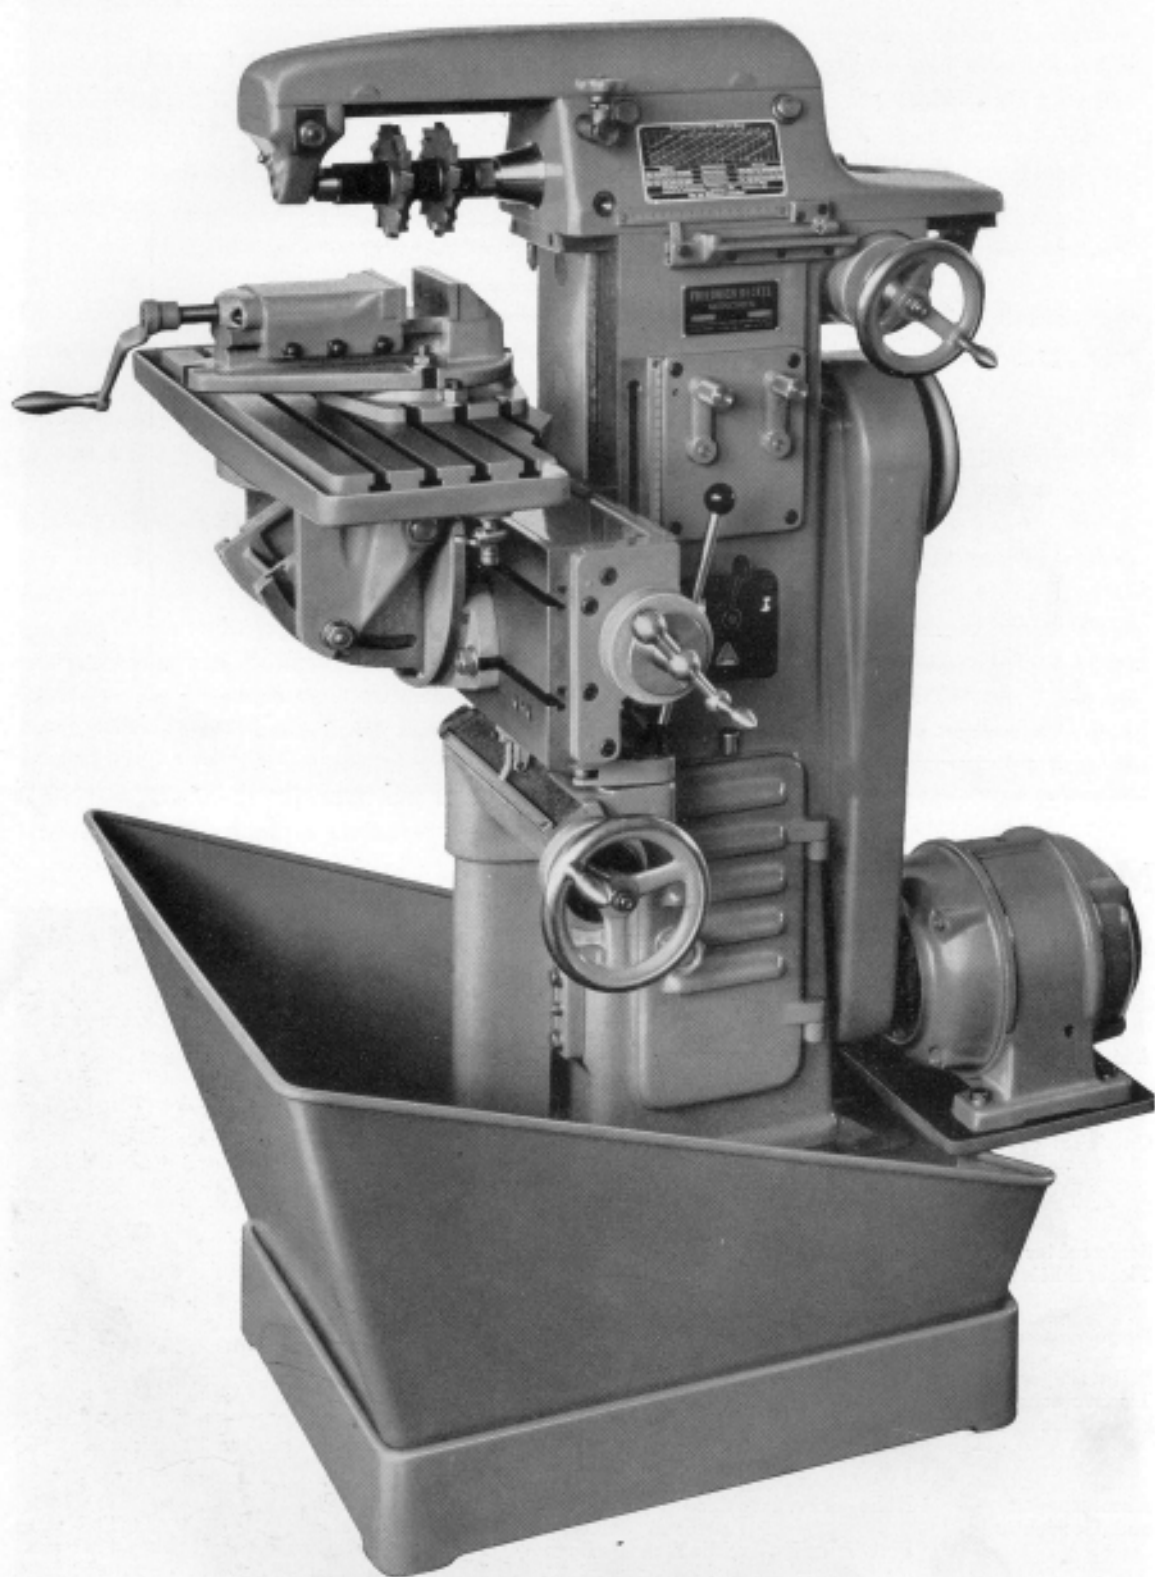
FP 1 Maschine mit Gegenhalter, schwenkbarem Winkeltisch mit Schraubstock
